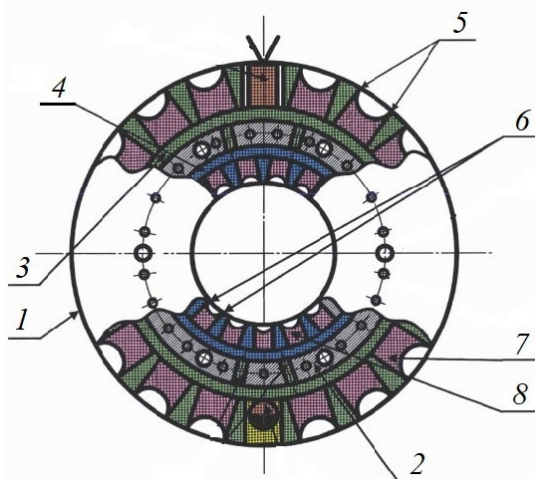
Общая схема устройства кассеты: 1 — стальной усеченный конус; 2 — разделяющая стенка; 3 — кольцевой прижимной заряд ВВ; 4 — кольцевой забойный заряд ВВ; 5 — прижимной цилиндрический отражатель; 6 — забойный цилиндрический отражатель; 7 — кумулятивный прижимной заряд ВВ; 8 — кумулятивный забойный заряд ВВ.
